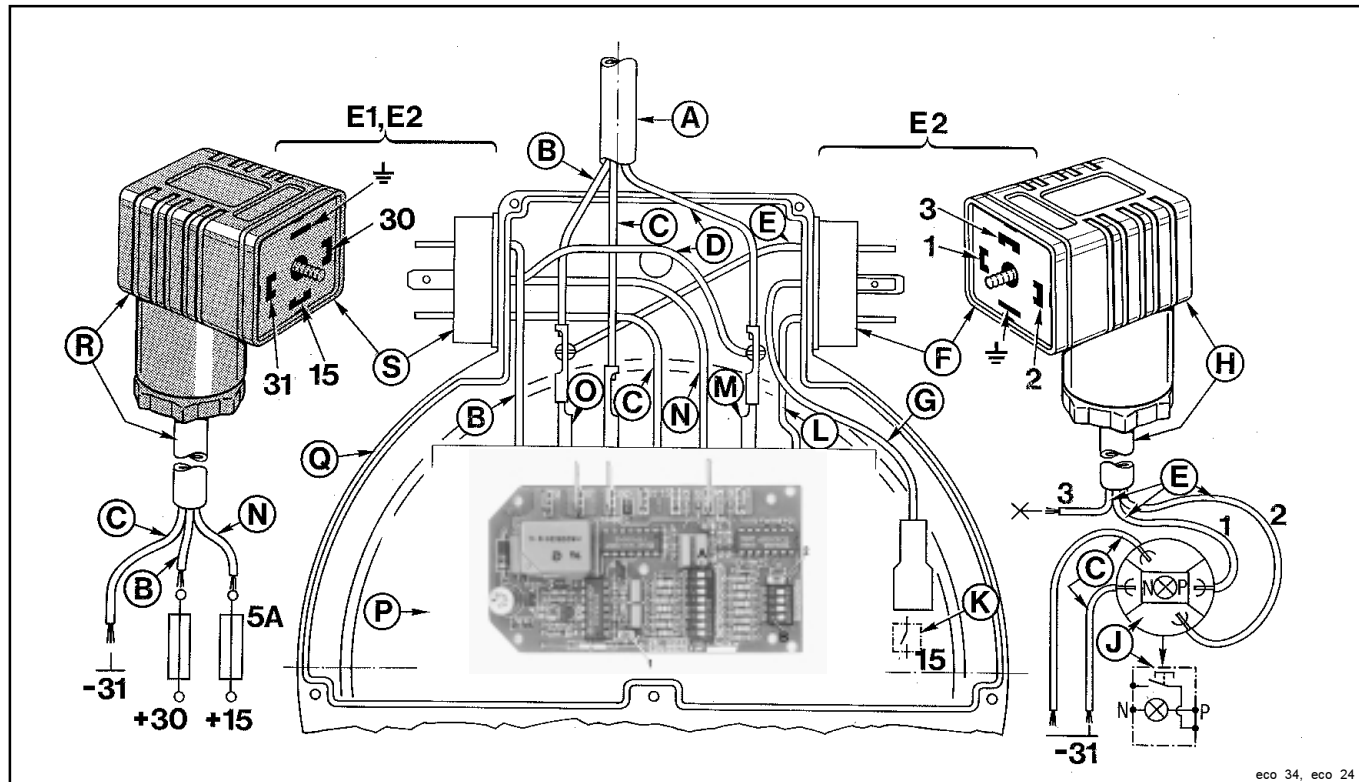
Anschlußschaltbild für Zugfahrzeuge
